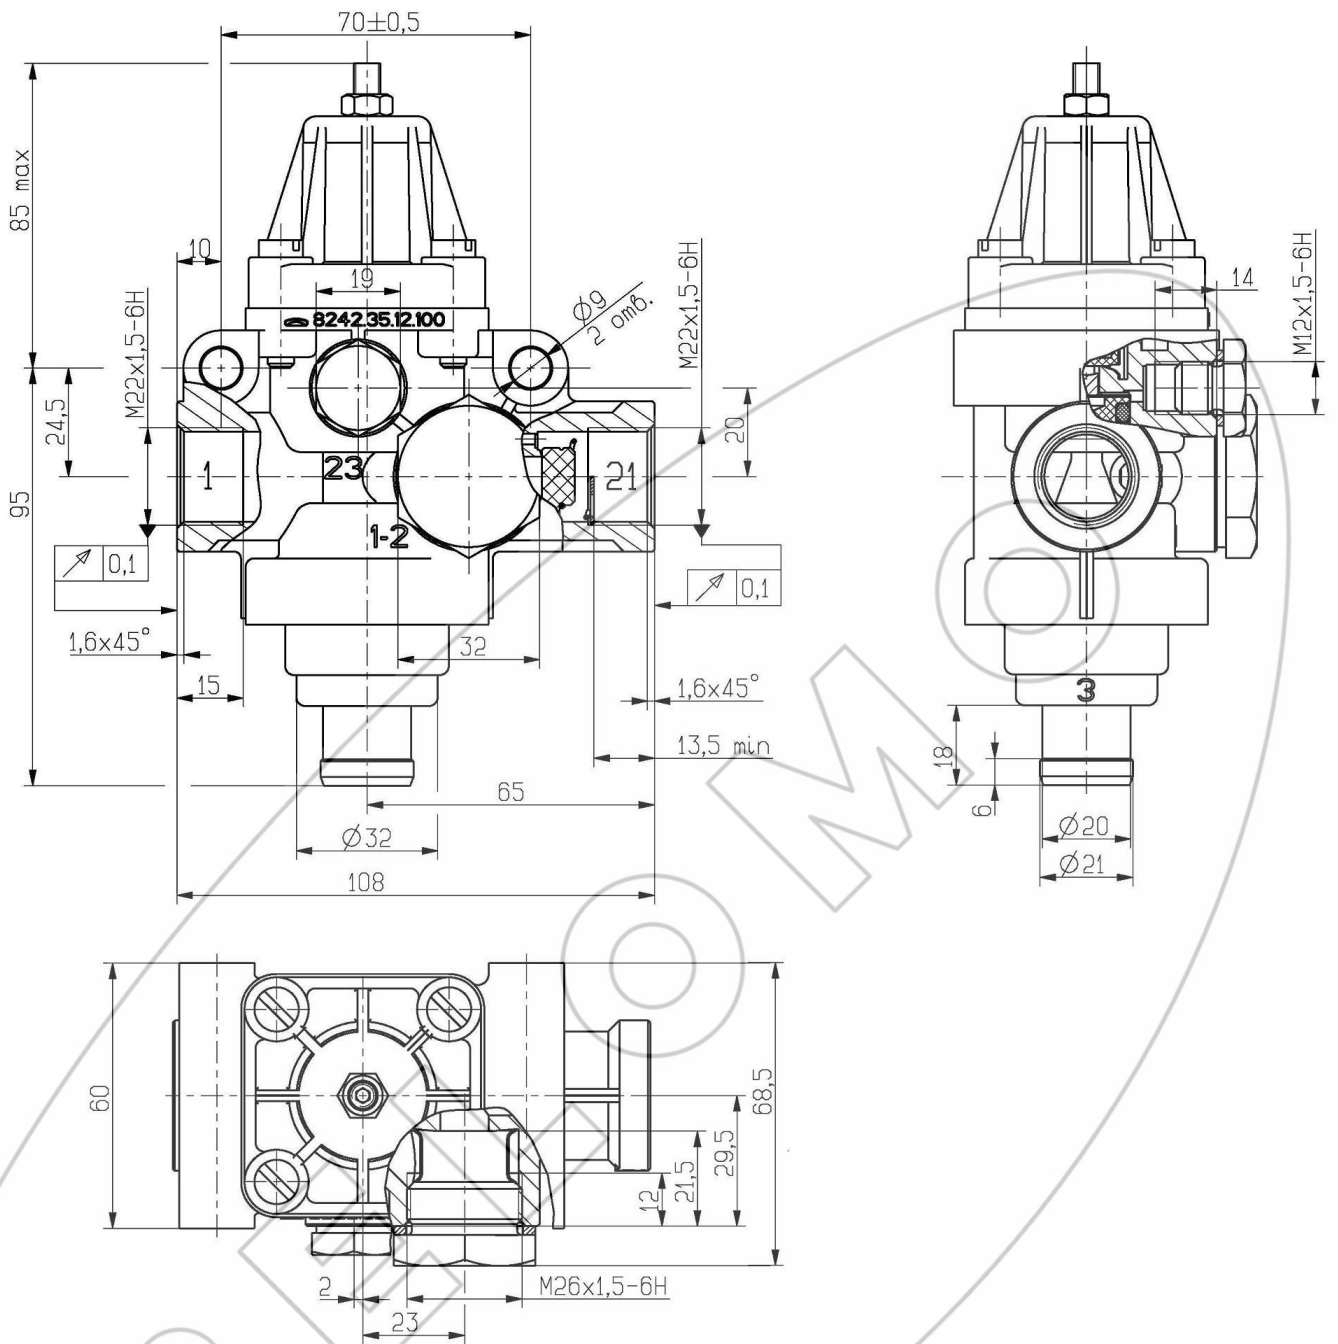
Габаритные и присоединительные размеры регулятора
